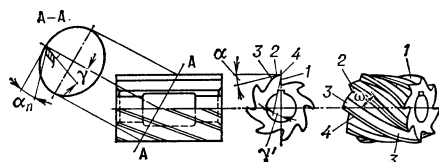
Геометрические параметры режущей части цилиндрической фрезы: 1 — передняя поверхность зуба; 2 — задняя поверхность зуба; 3 — затылочная поверхность зуба; 4 — винтовая главная режущая кромка зуба.
